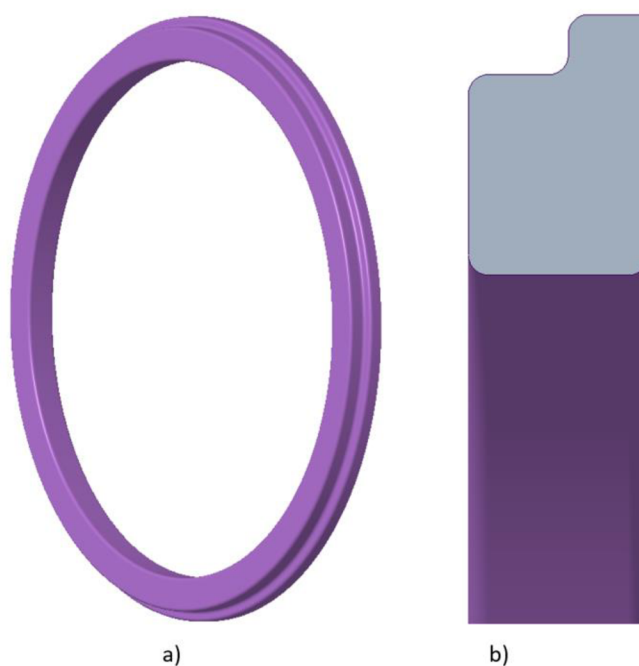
Pouzdro spojky vyobrazené a) v obecném pohledu b) v řezu
